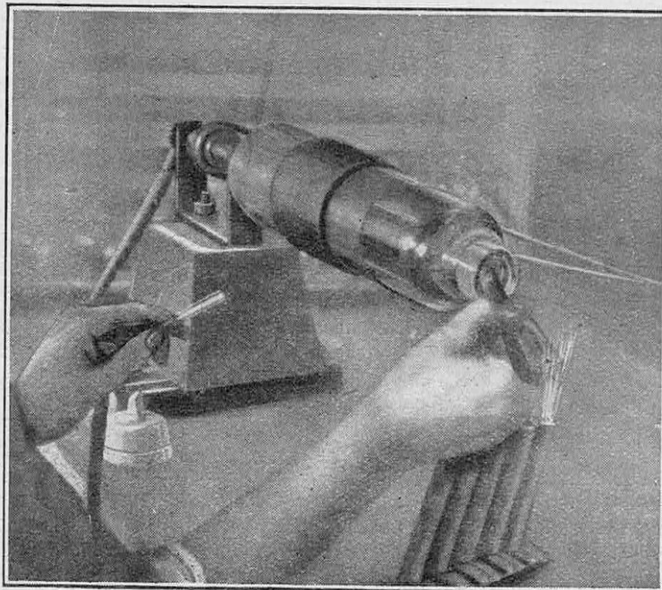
SOUDURE DES COLS DE DEUX BOUTEILLES
